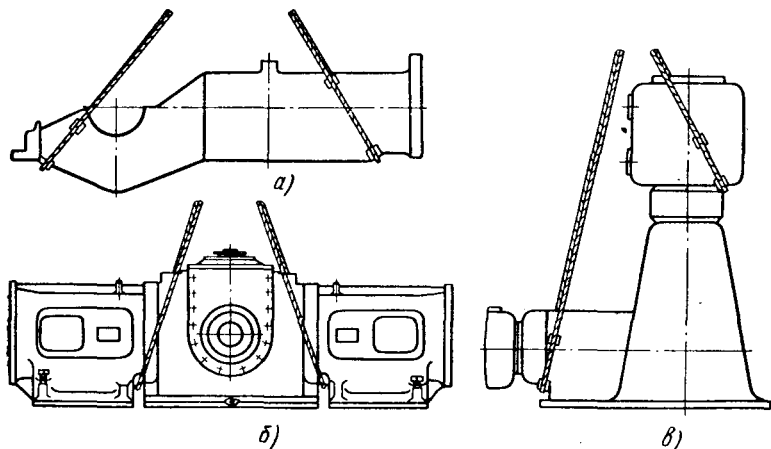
Схемы строповки рам компрессоров — горизонтального с односторонним расположением цилиндров (а) и прямоугольного в сборе (б) и оппозитного (в)
